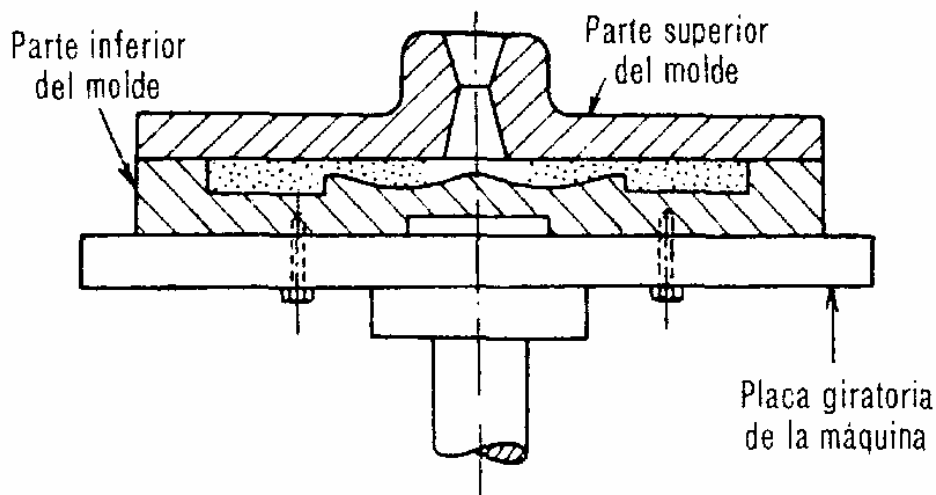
Moldeo de una pieza anular en coquilla de cavidad completa
